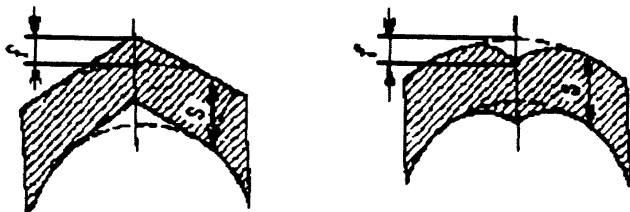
Увод (угловатость) кромок в сварных швах
